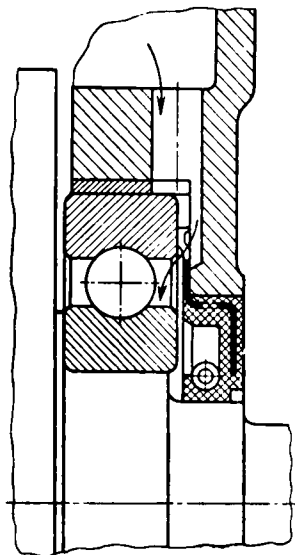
Правильное положение сальника коленчатого вала мотороллеров ВП-150 и В-150М относительно смазочного отверстия в картере двигателя
